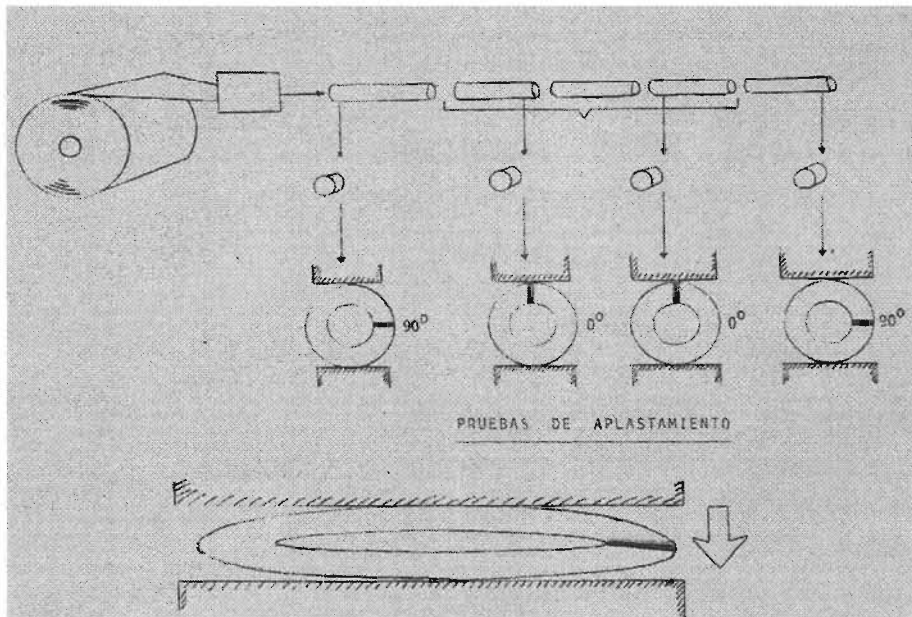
Muestra la colocación de la soldadura en una prueba de aplastamiento.
